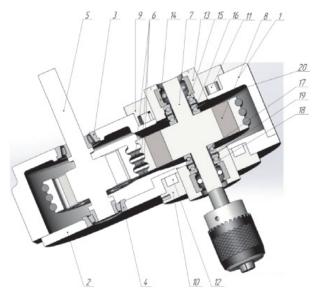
Устройство для вибрационного сверления: 1 — корпус; 2 — крышка корпуса; 3, 4 — подшипники; 5 — входной вал; 6 — гибкая связь; 7 — выходной вал; 8 — магниты; 9, 10 — магнитные корпуса; 11, 12 — магниты; 13 — гайка; 14 — подшипник; 15, 16, 17, 18 — упорные подшипники; 19, 20 — пружины
